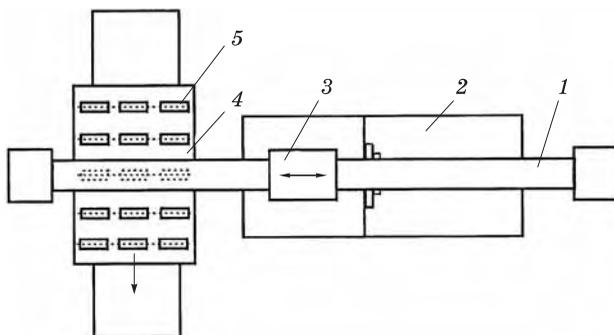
Схема использования циклического подающего устройства: 1 — токарный станок; 2 — порталный робот с перемещением по одной оси; 3 — тележка с механической рукой; 4 — палета; 5 — детали на палете, уложенные рядами
